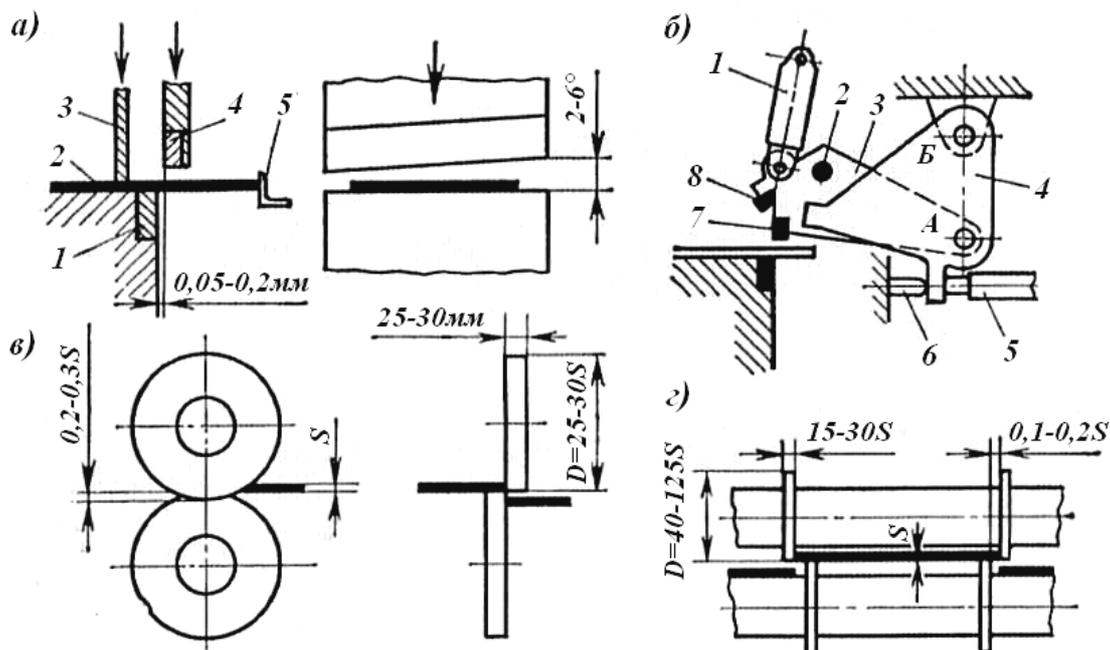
Схема резки металла на ножницах различных типов: а – гильотинные ножницы с прямым резом; 1 – нижний нож; 2 – лист; 3 – прижим; 4 – верхний нож; 5 – упор; б – гильотинные ножницы с прямым резом со скосом кромки; 1 – гидроцилиндр; 2 – упор; 3 – ножедержатель; 4 – деталь; 5 – прижим; б – упор; 7 – прямой нож; 8 – косой нож; в – дисковые ножницы; г – многодисковые ножницы
